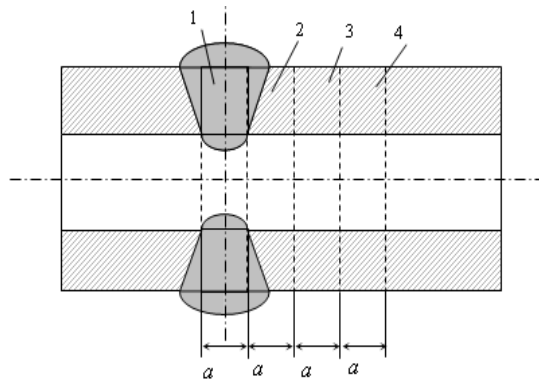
Эскиз фрагмента трубы со сварным швом и околошовной зоной
